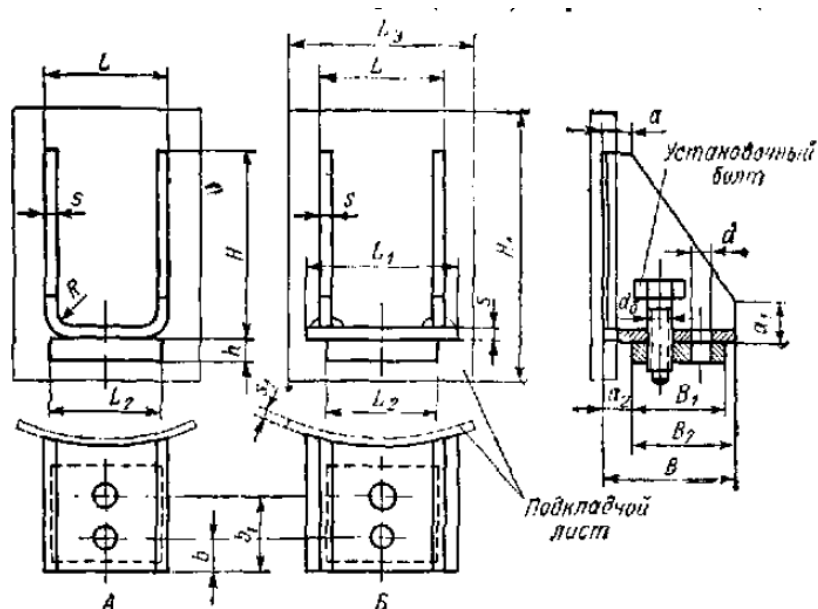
Сварные опоры вертикального аппарата
